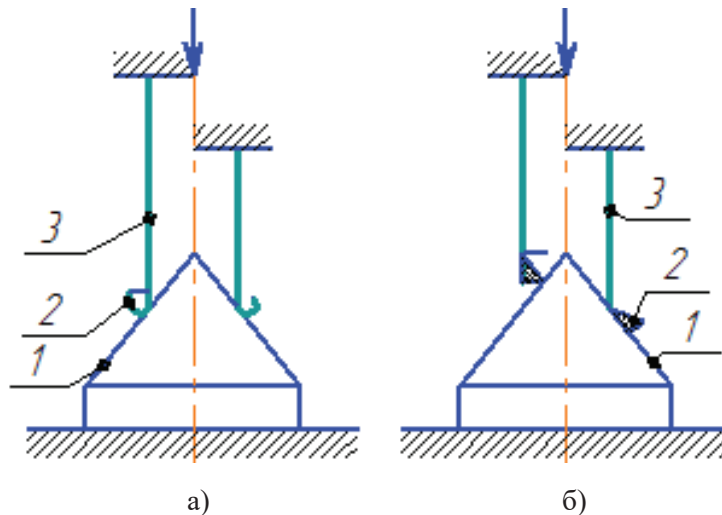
Роздавання з попередньо підготовленої трубчастої заготовки: а – заготовка вивернута на зовні; б – попереднє осадження заготовки
